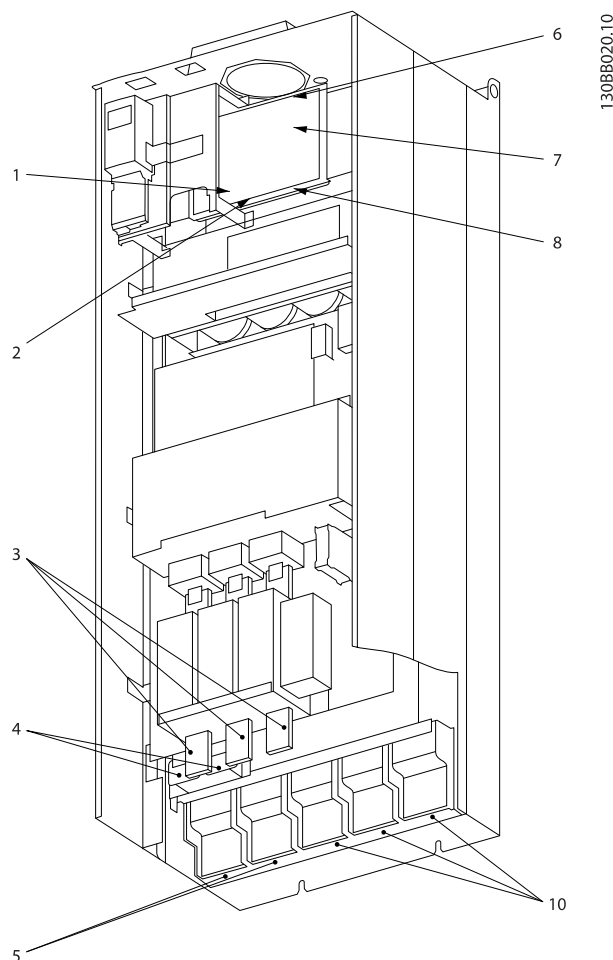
Poziția bornelor de împământare IP00, dimensiuni de carcasă D
